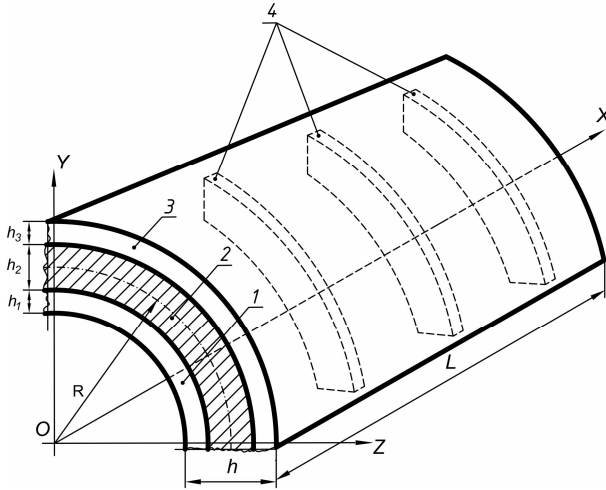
Конструкція тришарової оболонки: 1 – внутрішній шар; 2 – заповнювач; 3 – зовнішній шар; 4 – армуючі ребра
